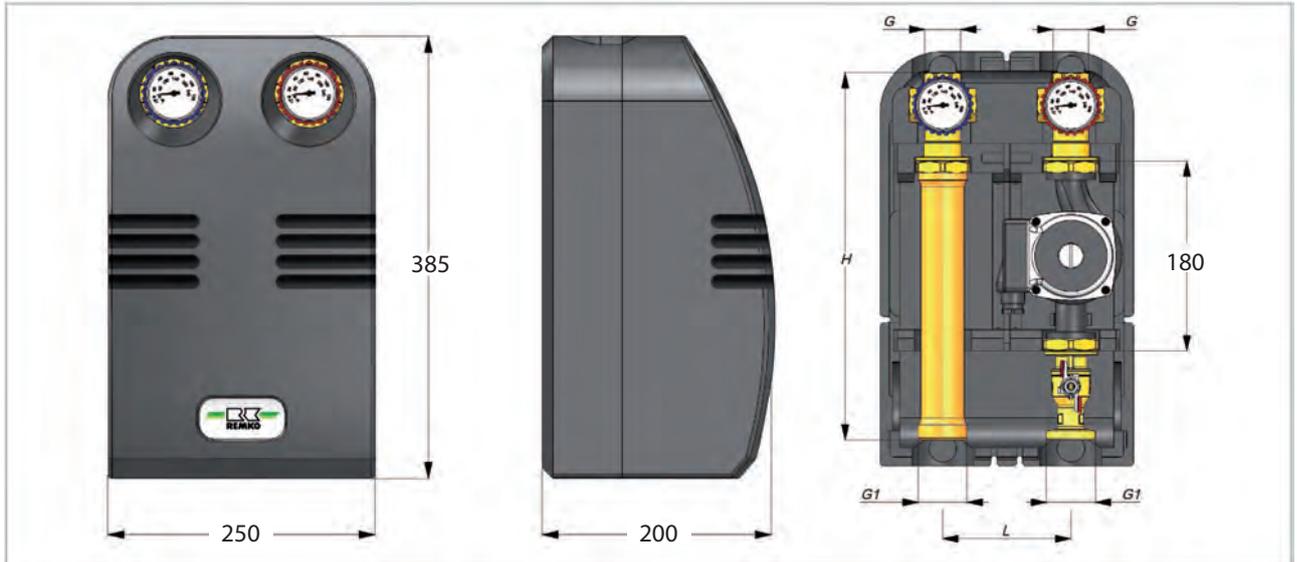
Geräteabmessungen Pumpengruppe HGU
